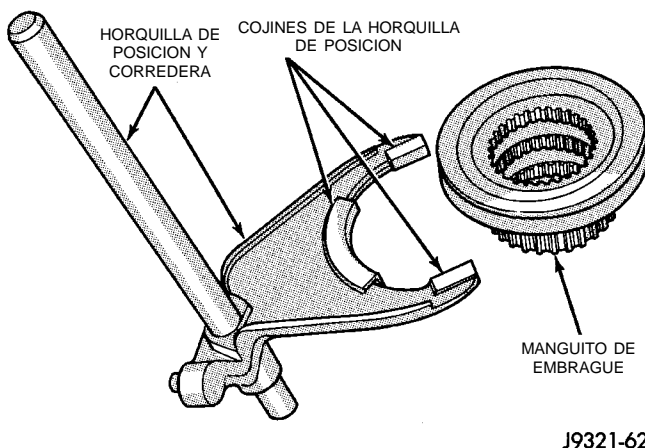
Ensamblaje de la horquilla de posiciones y el manguito de embrague
